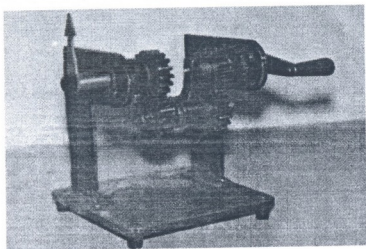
Макет планетарной передачи с эллиптическими цилиндрическими колесами
